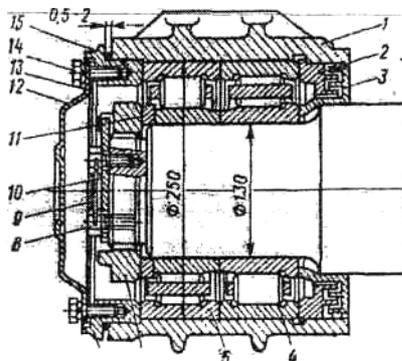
Букса грузового вагона с двумя цилиндрическими подшипниками с торцевым креплением корончатой гайкой
